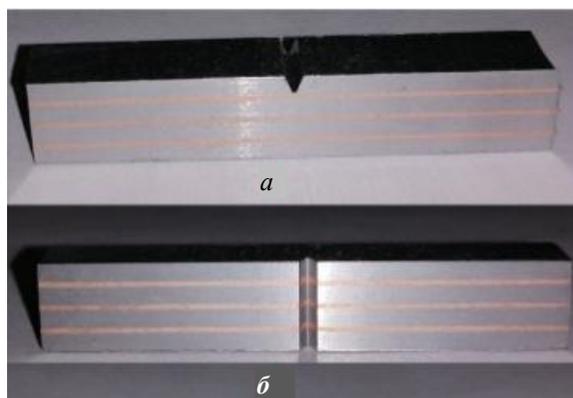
Общий вид образцов стали 3–меди М1 для испытаний по Шарпи:
